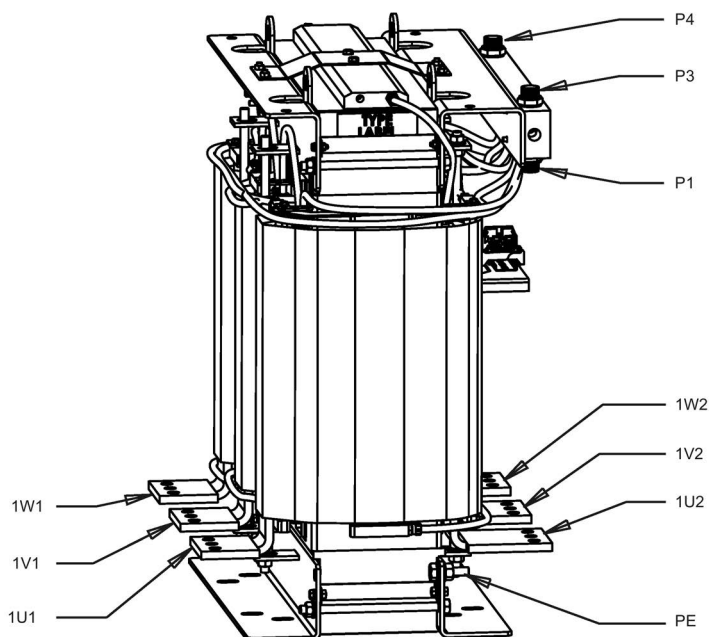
Обзор интерфейсов дросселя фильтра, типоразмер JIL, действителен для номеров по каталогу 6SL3005-0DE41-4AA0 и 6SL3005-0DG41-6AA0
